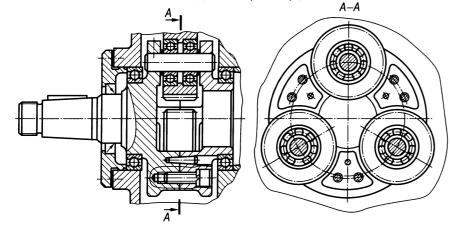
Разъемный вал-водило планетарного зубчатого редуктора
